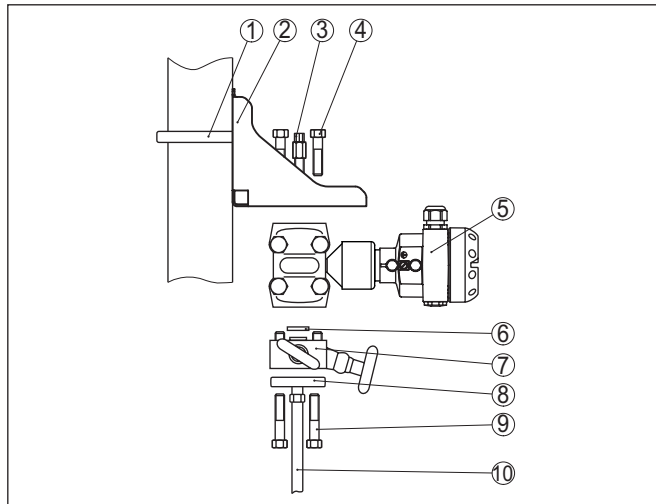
Disposizione di montaggio in caso di montaggio su tubo
